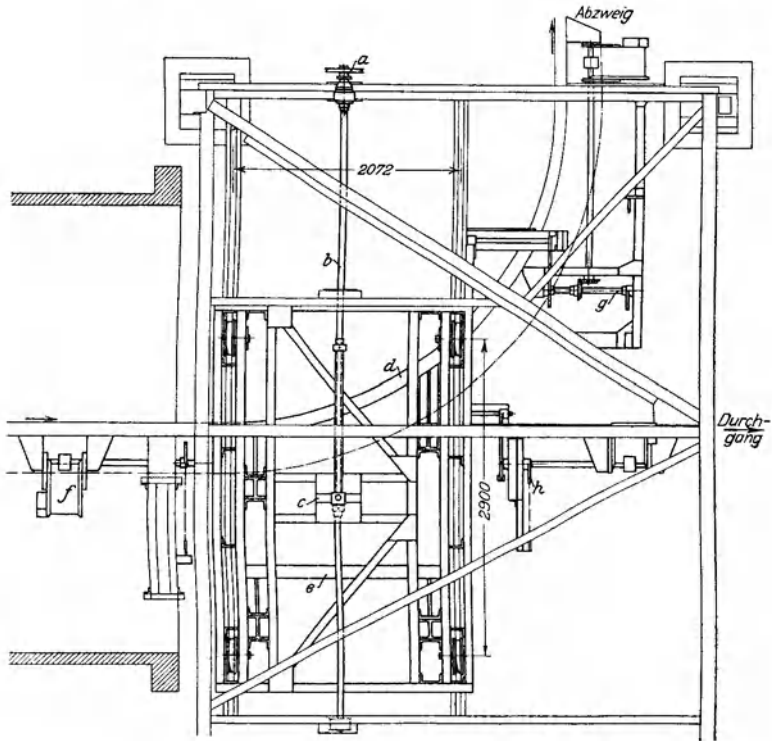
Grundriß einer Schiebeweiche (Kaiser & Co.).
